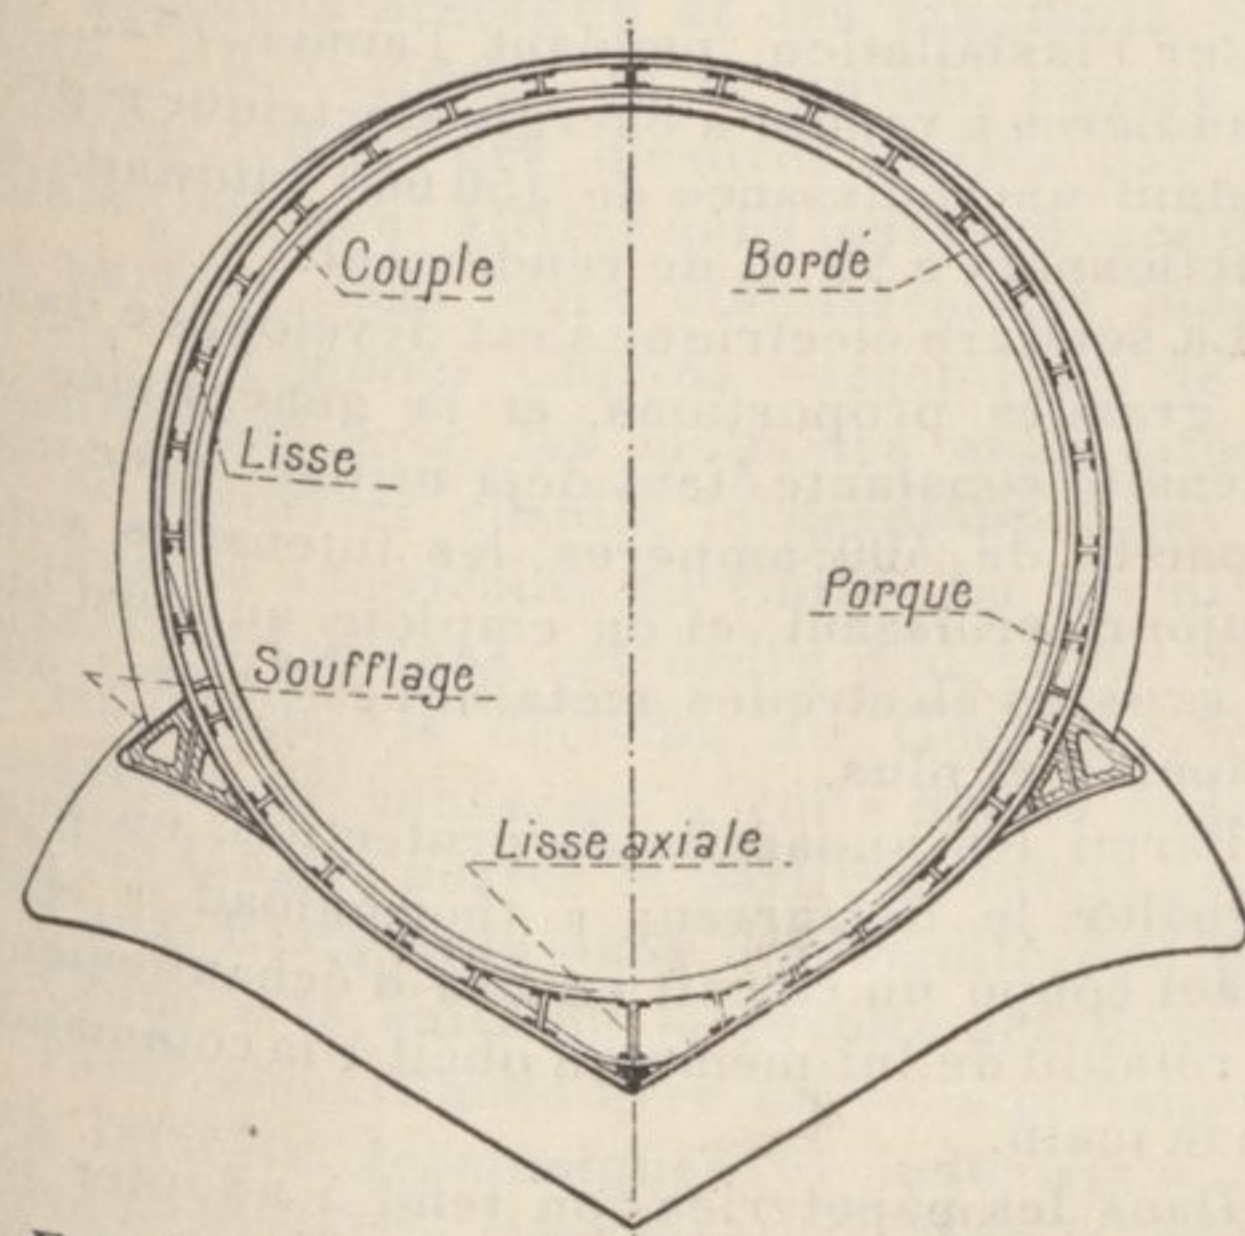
Coupe transversale d'une coque flexible d'hydravion.
